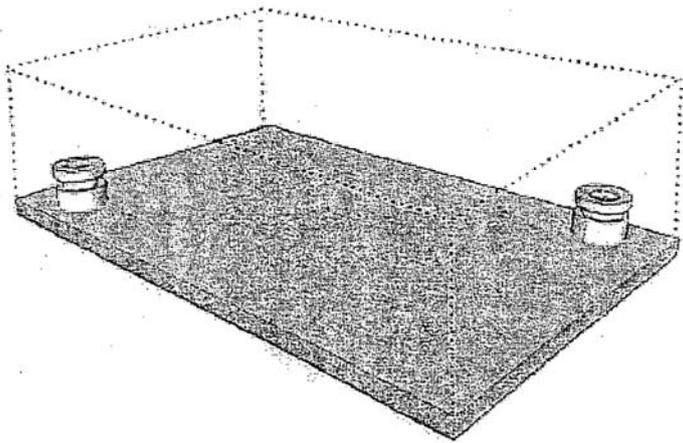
Muestra la posición de la carcasa en su lugar sobre la placa de base
